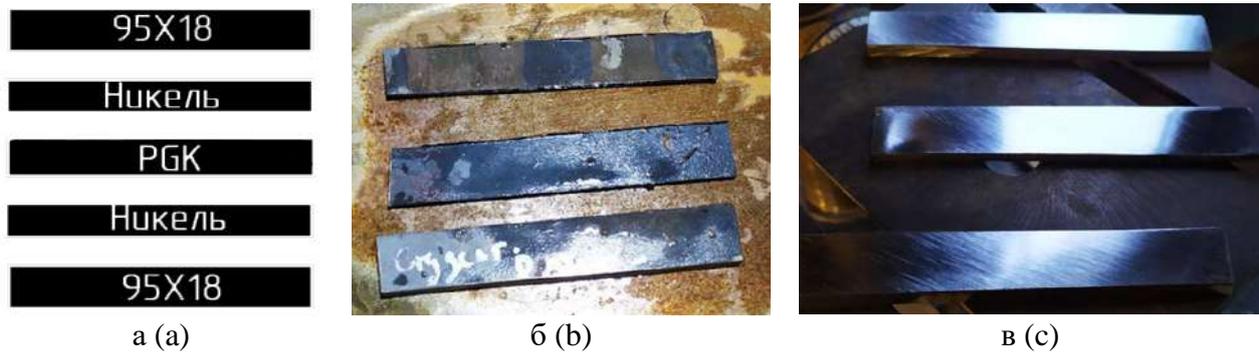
Листовые заготовки для изготовления клинка ножа: а – схема расположения заготовок; б – необработанные заготовки; в – заготовки после шлифования
